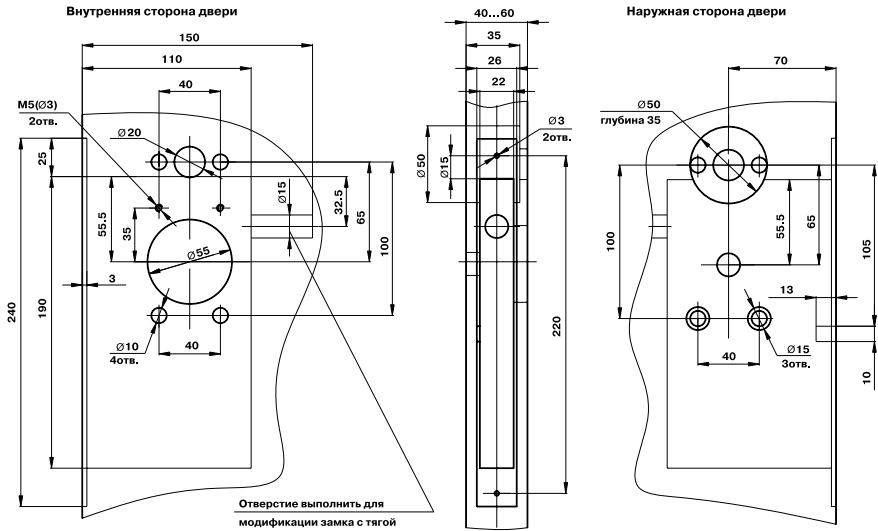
Разметка под установку замка на левостороннюю дверь
